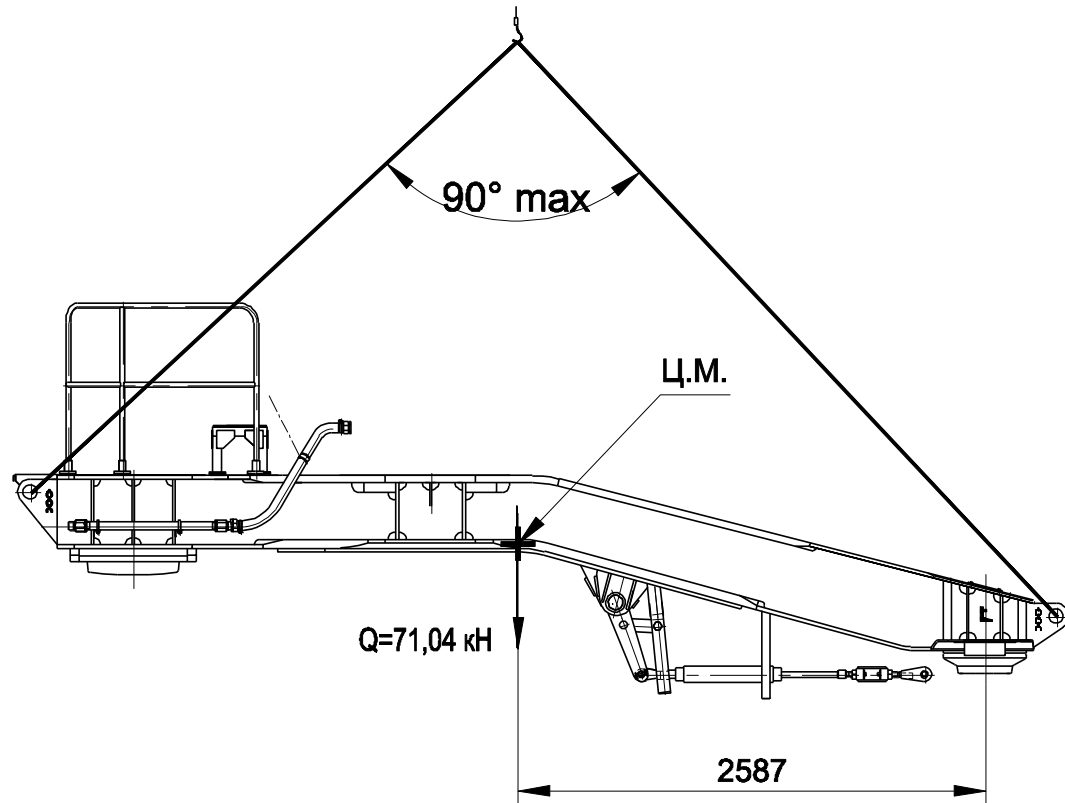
Схема строповки соединительной балки при демонтаже
